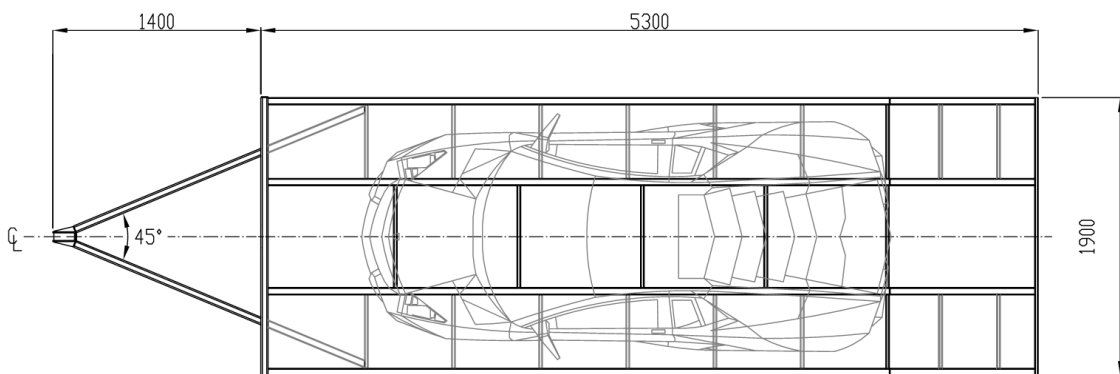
Vista Planta de remolque con dimensiones preliminares
